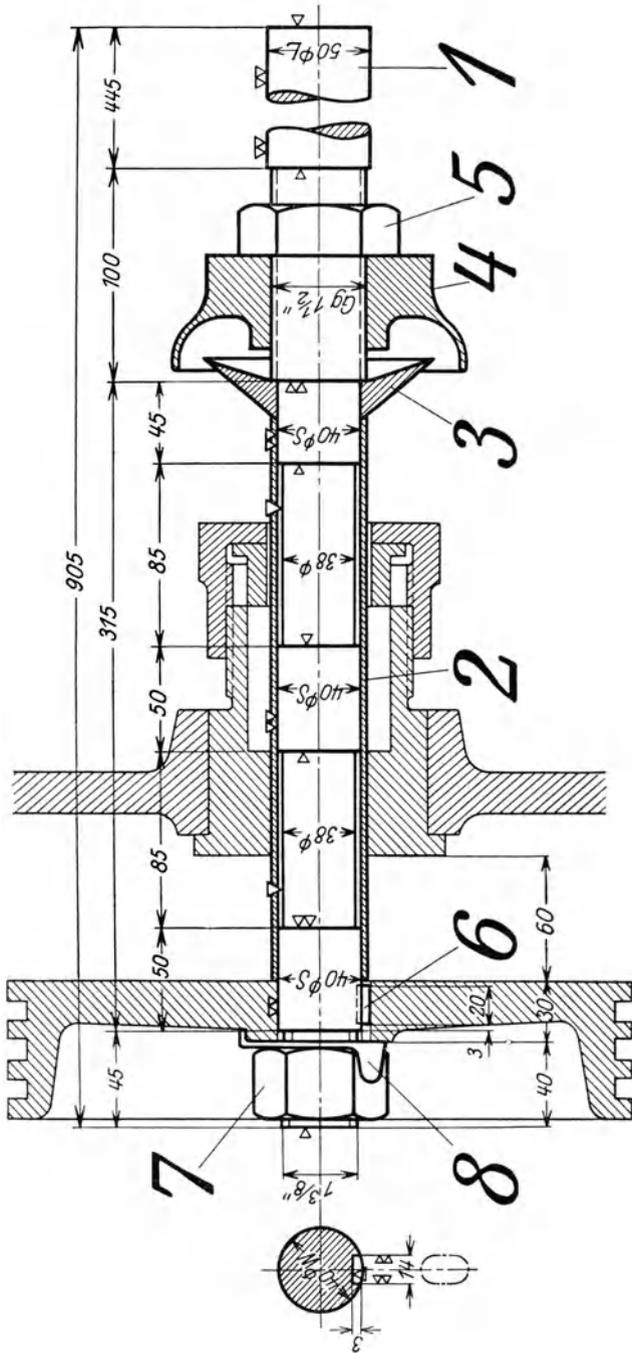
Gesamtzeichnung einer Spindel, gleichzeitig Werkzeugzeichnung für Teil I.
